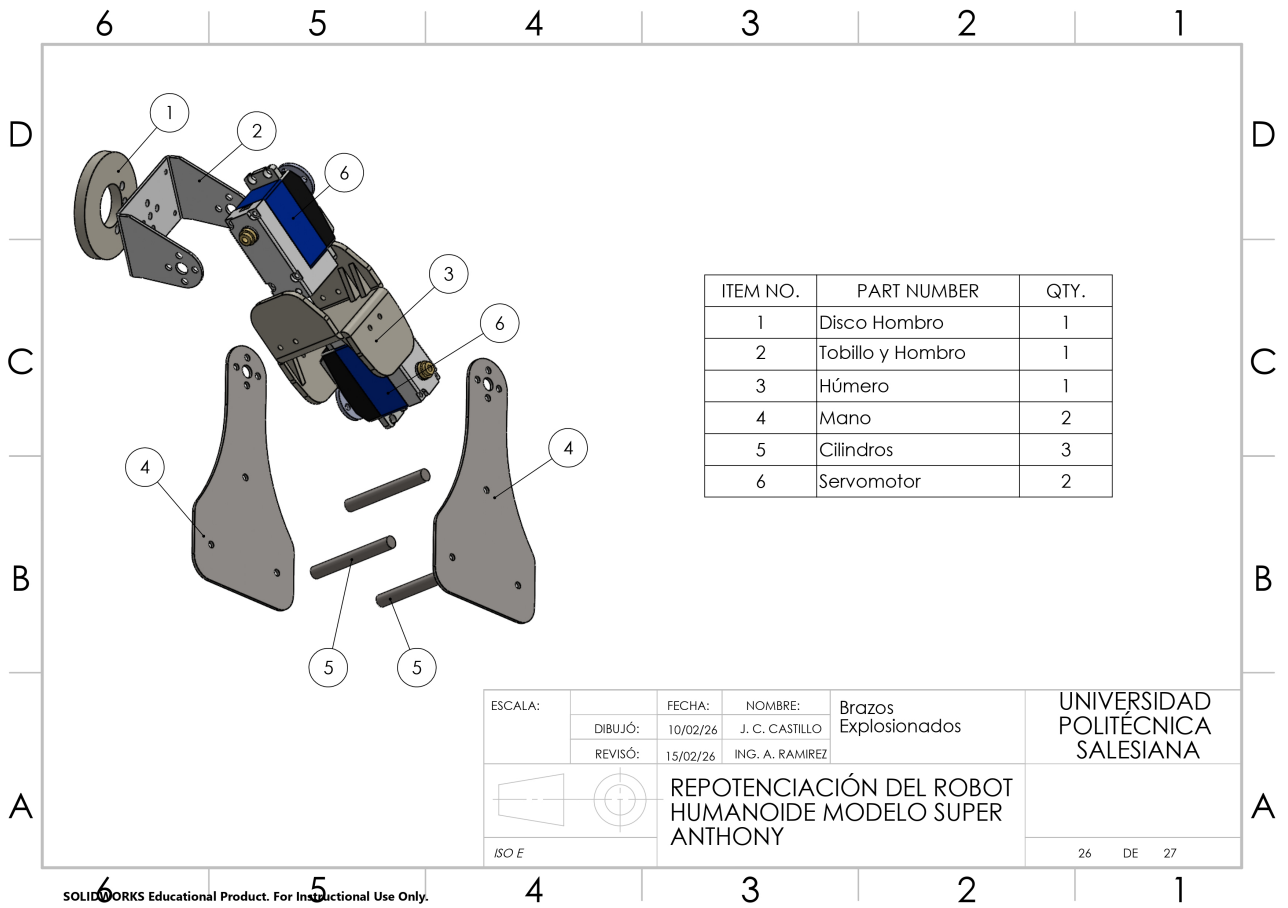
Lámina acotada de la vista explosionada del ensamble de los brazos del robot humanoide, por J. Castillo y B. Gualle, Solidworks
